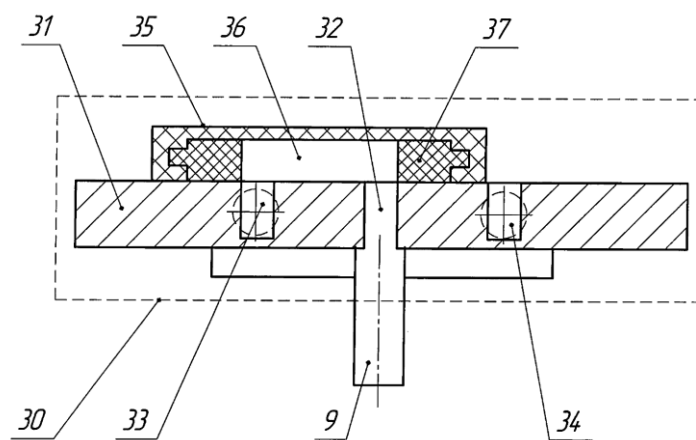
Пневморозподілювач вакуумметричного тиску пульсатора: 9 - патрубок; 31 - підстава; 32, 33 і 34 - паз; 35 - повзун; 36 - паз; 37 - вкладиш
